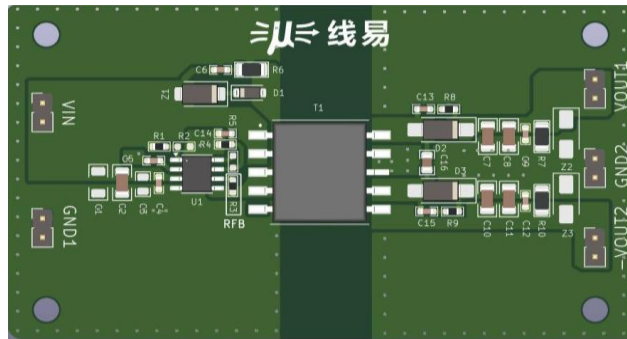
PCB 示意图 (尺寸: 45 x 80mm)
